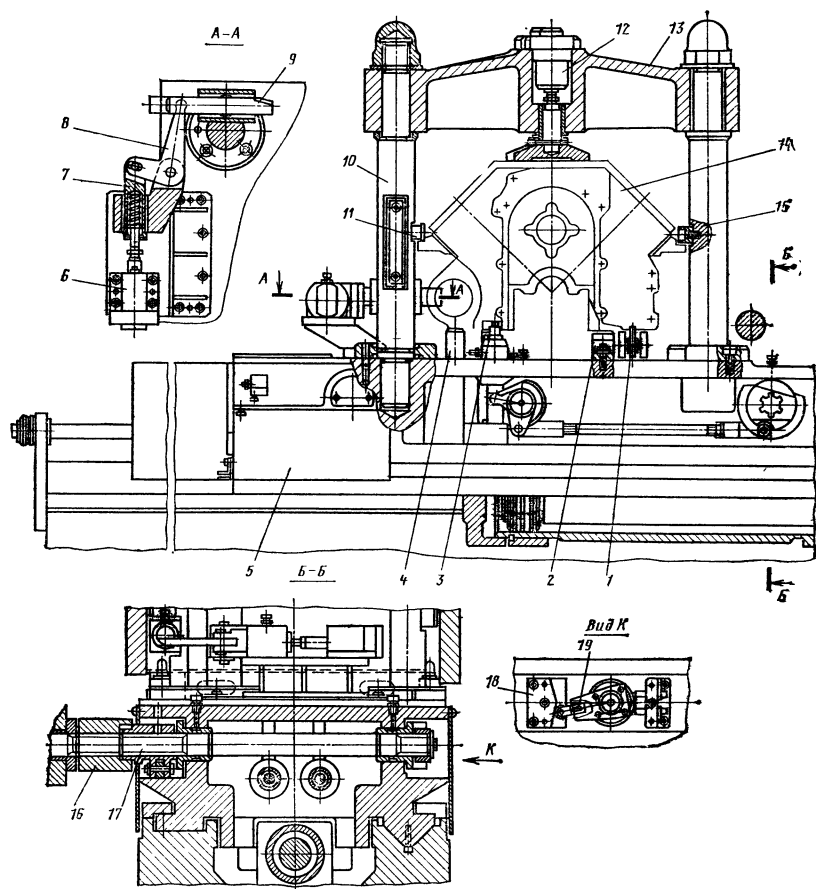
Компонка приспособления агрегатно-фрезерного станка с силовым столом рабочей подачи:
